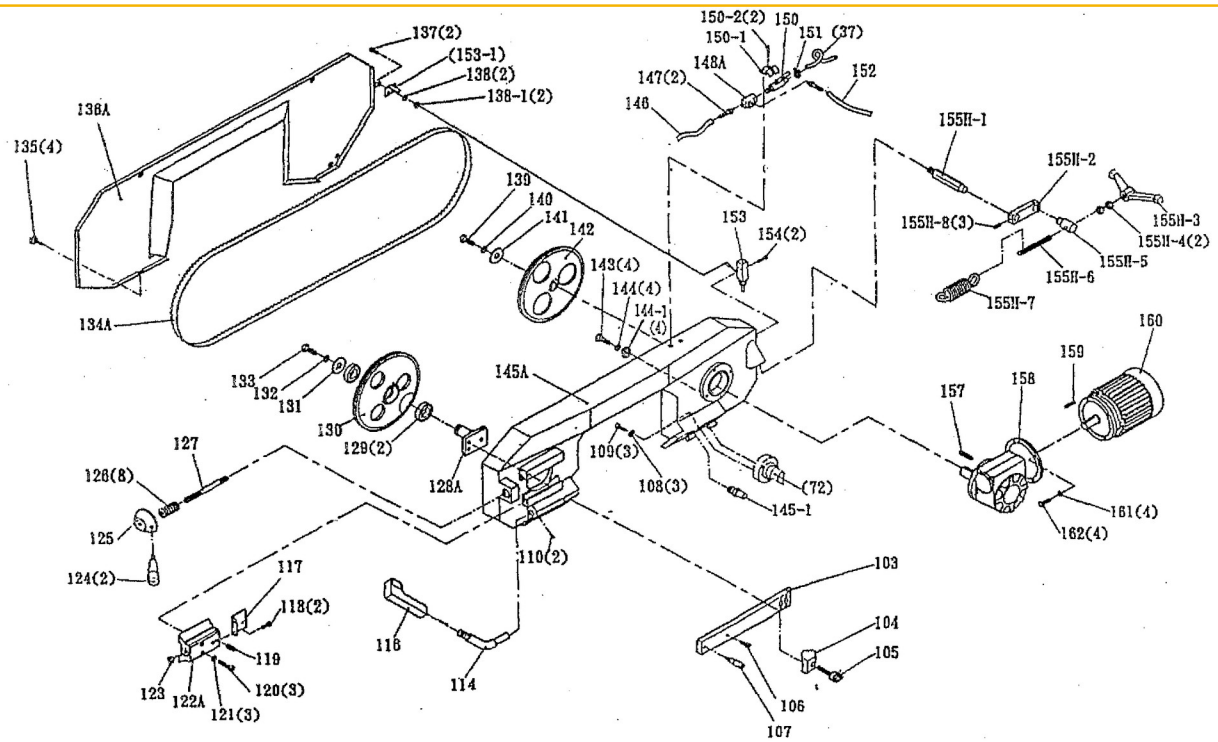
Figura 3 — Arco da serra, transmissão e motor
